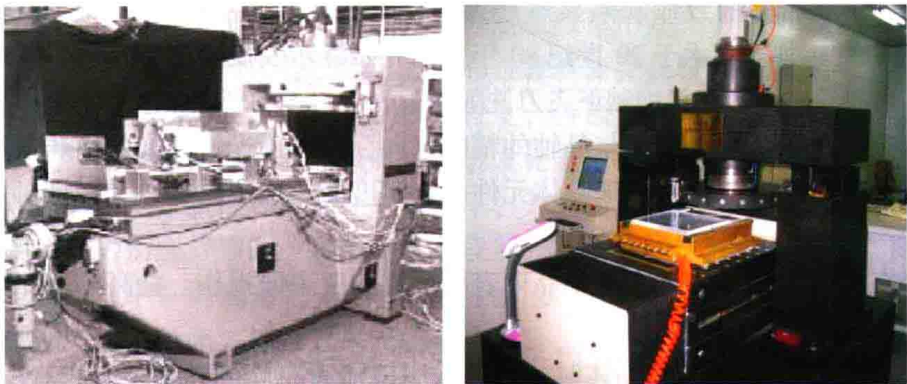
KDP 晶体超精密飞切加工机床结构示意图
